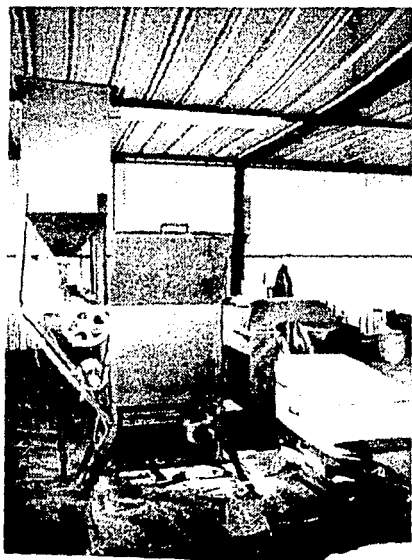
Muestra la máquina viendo el motor y la polea, el mecanismo de vaivén y el ventilador que separa la semilla reventada
